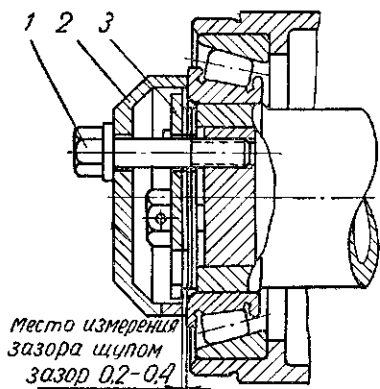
Приспособление для проверки осевого зазора в конических роликоподшипниках конечной передачи:
